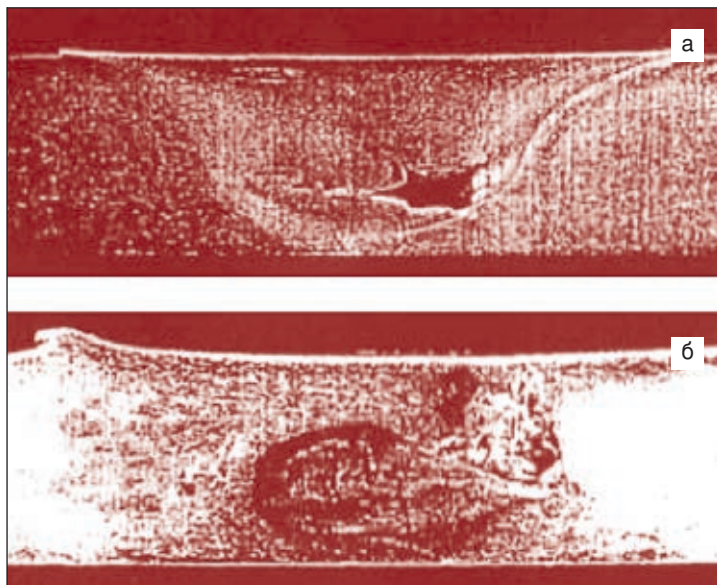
Дефекты, образующиеся в швах из алюминиевых сплавов, полученных сваркой трением с перемешиванием, вызванные неблагоприятными условиями перемешивания металла: а — при недостаточной скорости вращения инструмента или большом зазоре между кромками; б — при избыточной скорости вращения инструмента по сравнению с линейной скоростью его перемещения
